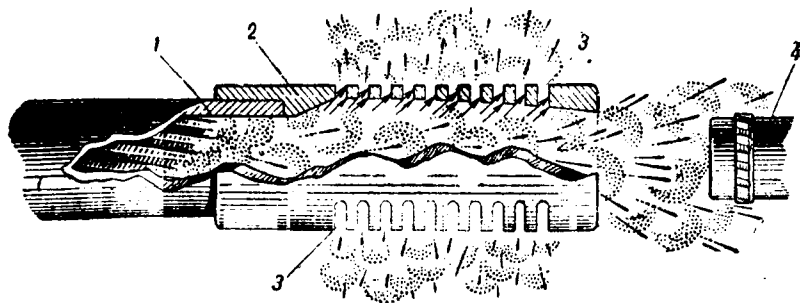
Схема дульного тормоза (вид сверху). 1—ствол; 2—надульник; 3—каналы для выхода пороховых газов; 4—снаряд в момент вылета из тормоза.
